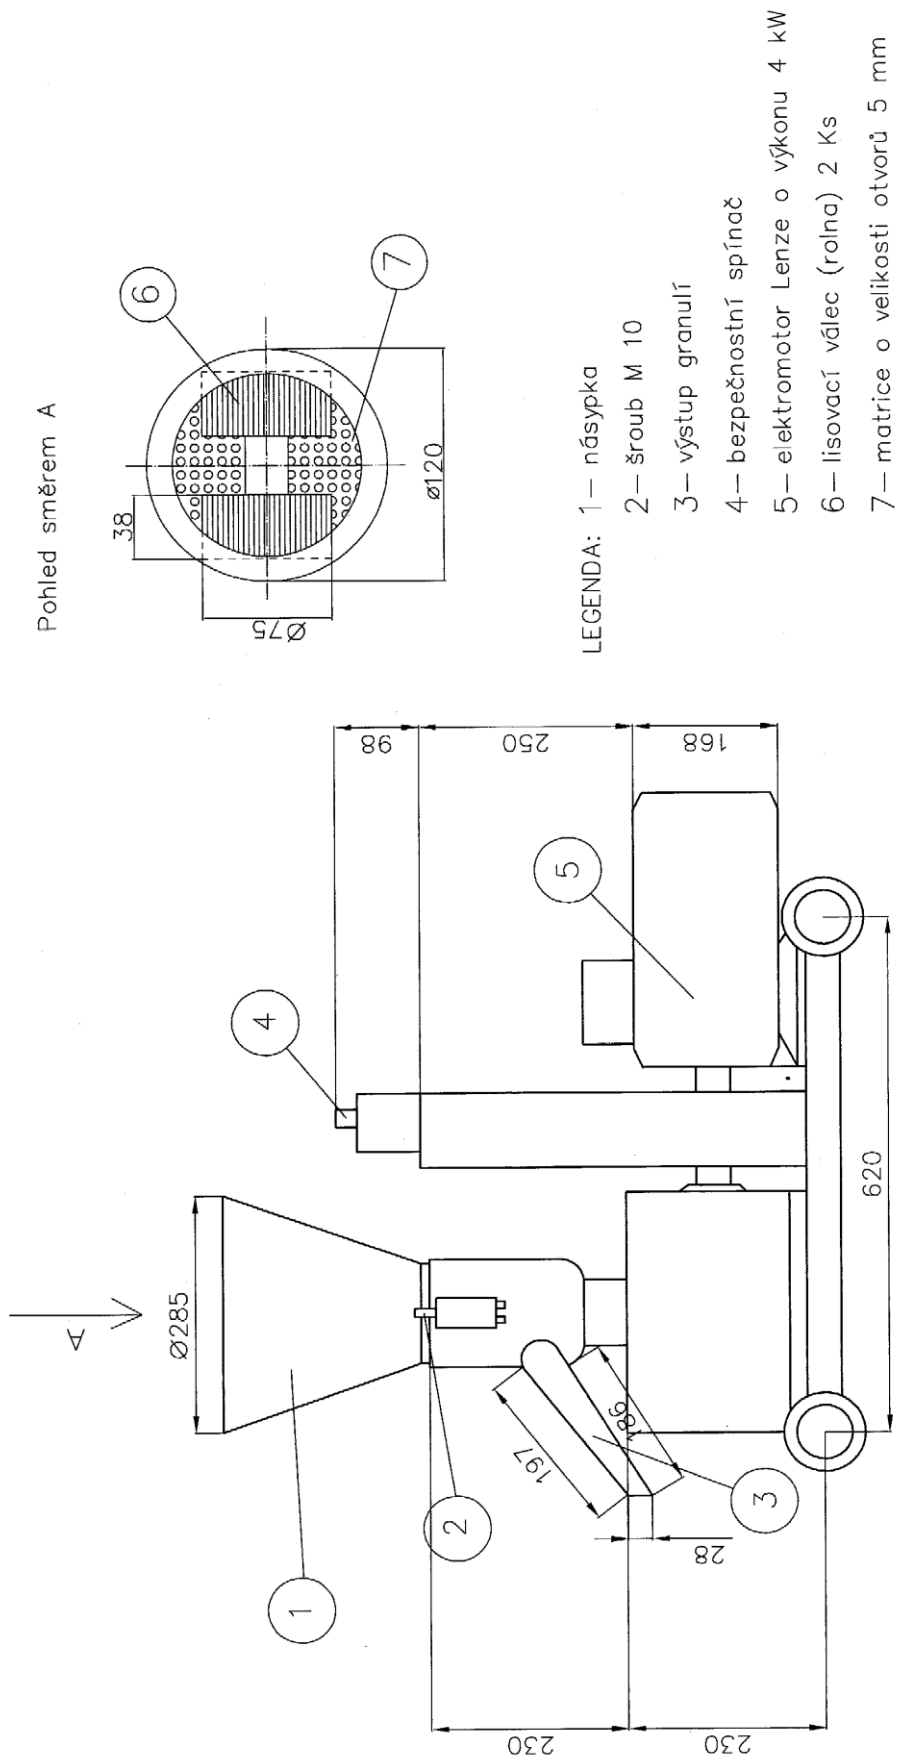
Briketovací lis JGE 120 – 6100 - detail
